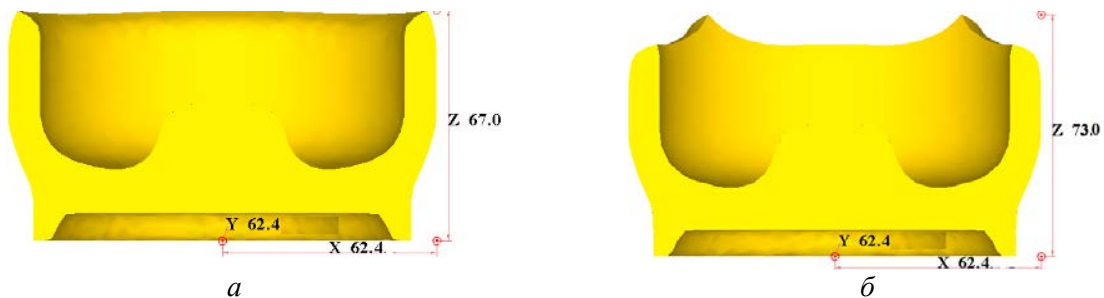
Форма і зовнішні розміри половин напівфабрикатів в розрізі після видавлювання: *a* - заготовки круглого перерізу, *б* - заготовки квадратного перерізу
